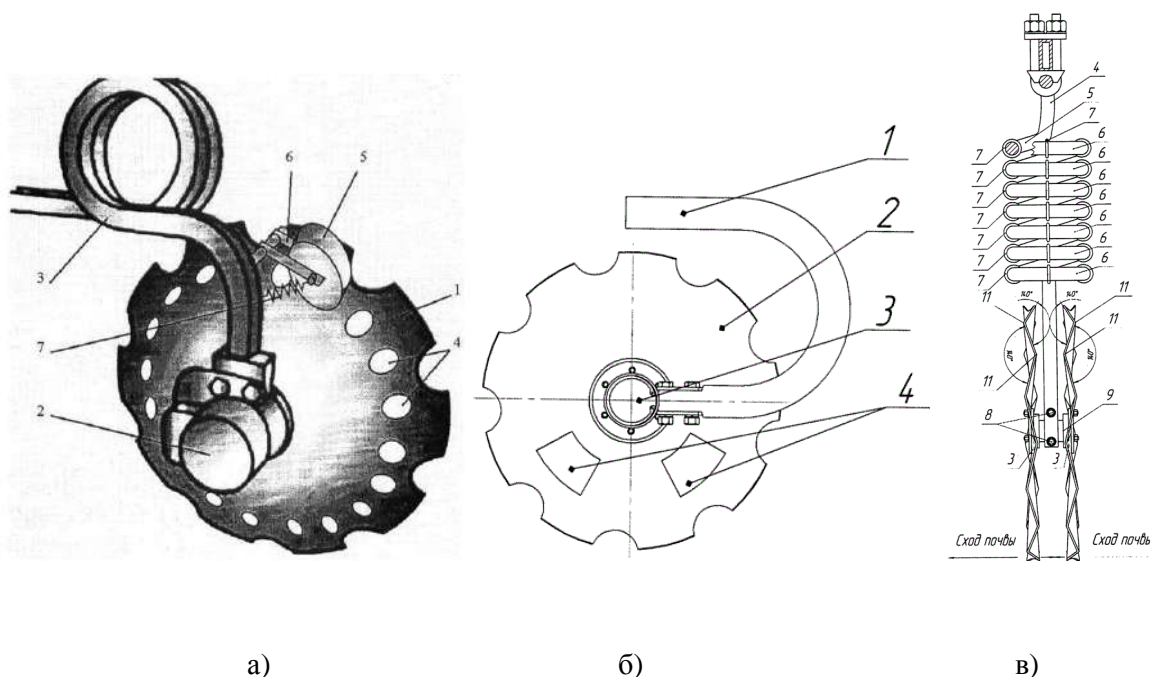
Конструктивная схема колебательного рабочего органа дискового орудия: а) на стойке типа Vaderstad; б) на S-образной подвеске; в) стойка в виде цилиндрической пружины с витками
